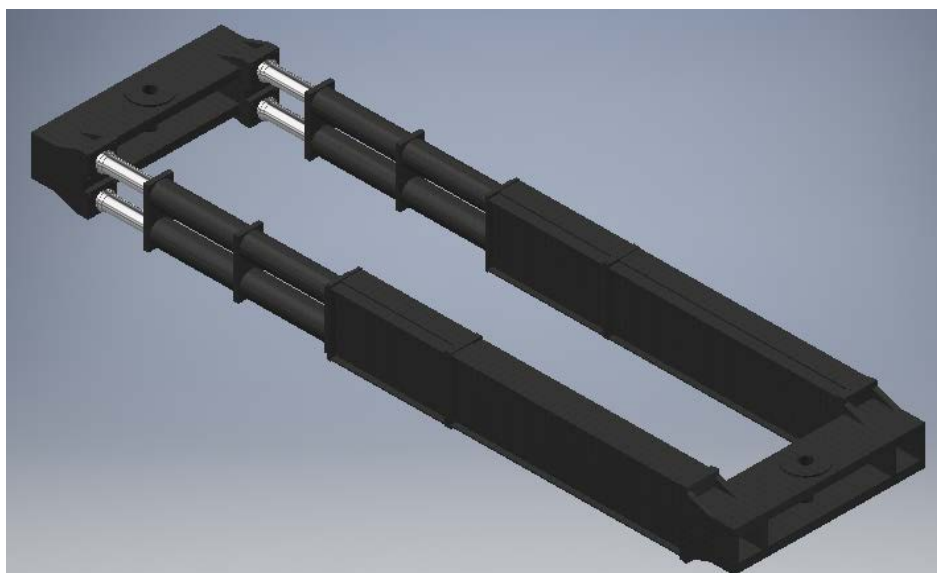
Vista isométrica máquina cabeçotes, pistões e vigas de 3 metros e 6 metros
